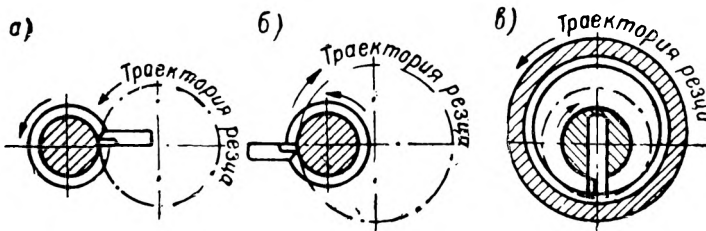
Способы обработки при вихревом нарезании резьбы.
